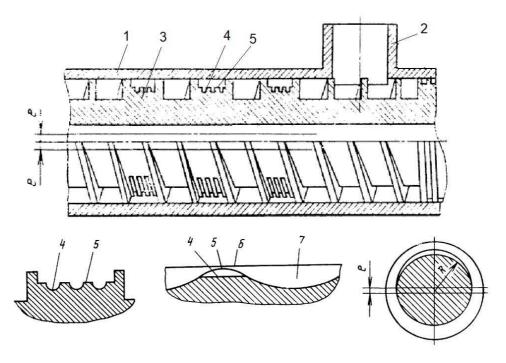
Экструдер для приготовления корма по А.С. 1493240 [2]: 1 — корпус; 2 — загрузочная воронка; 3 — шнек; 4 — проточка; 5 — сердечник;
